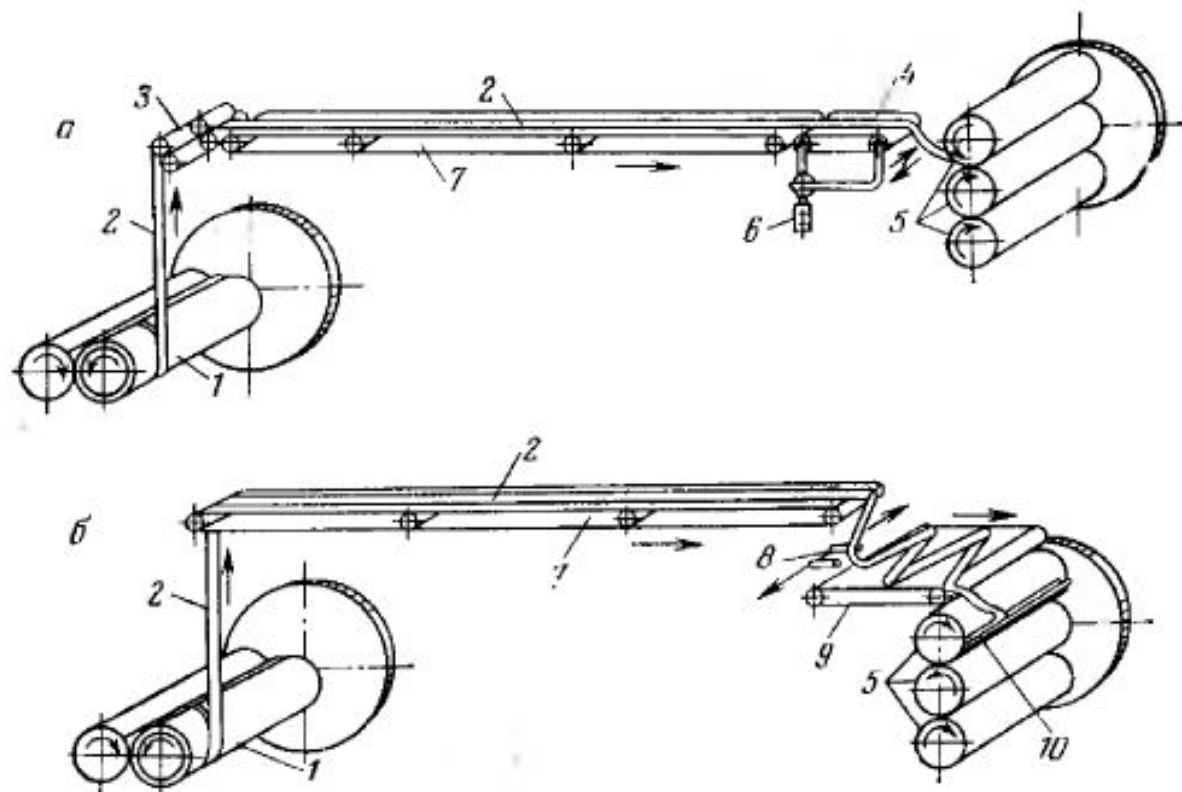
Схемы непрерывного питания трехвалкового каландра с распределением резиновой смеси по поверхности валка каландра с помощью качающегося транспортера (а) или распределительных роликов и дополнительного ленточного транспортера (б):
